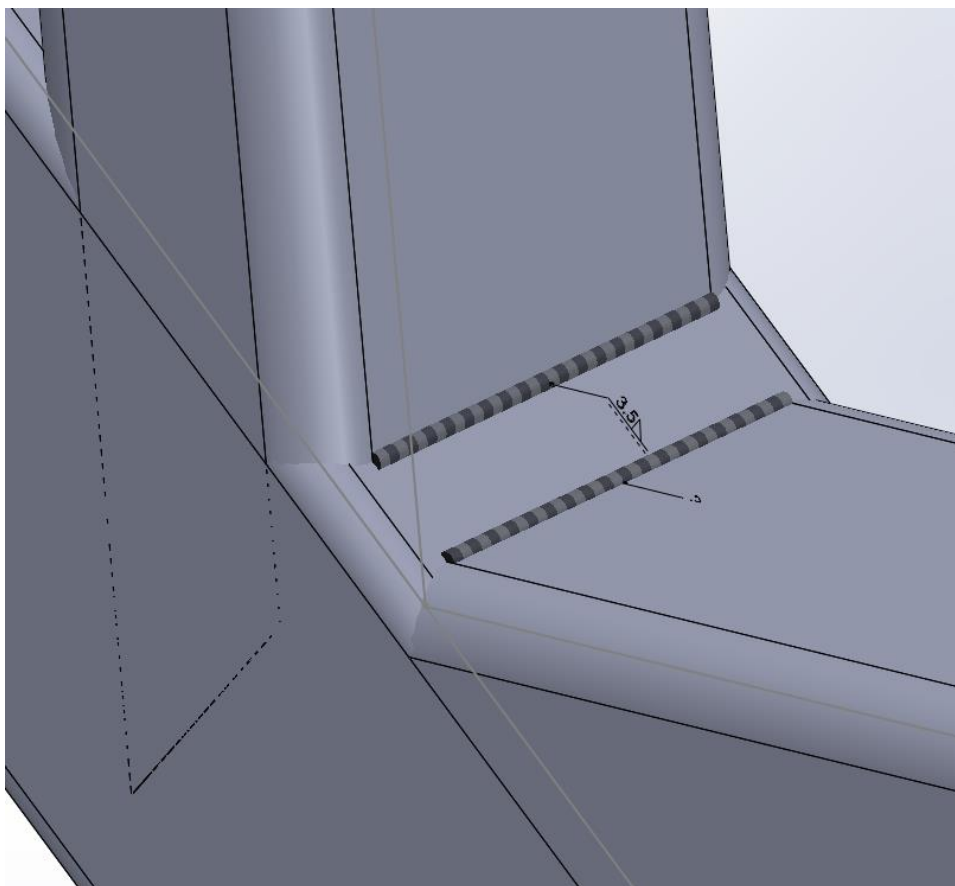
Visualización del cordón de soldadura ejecutado
